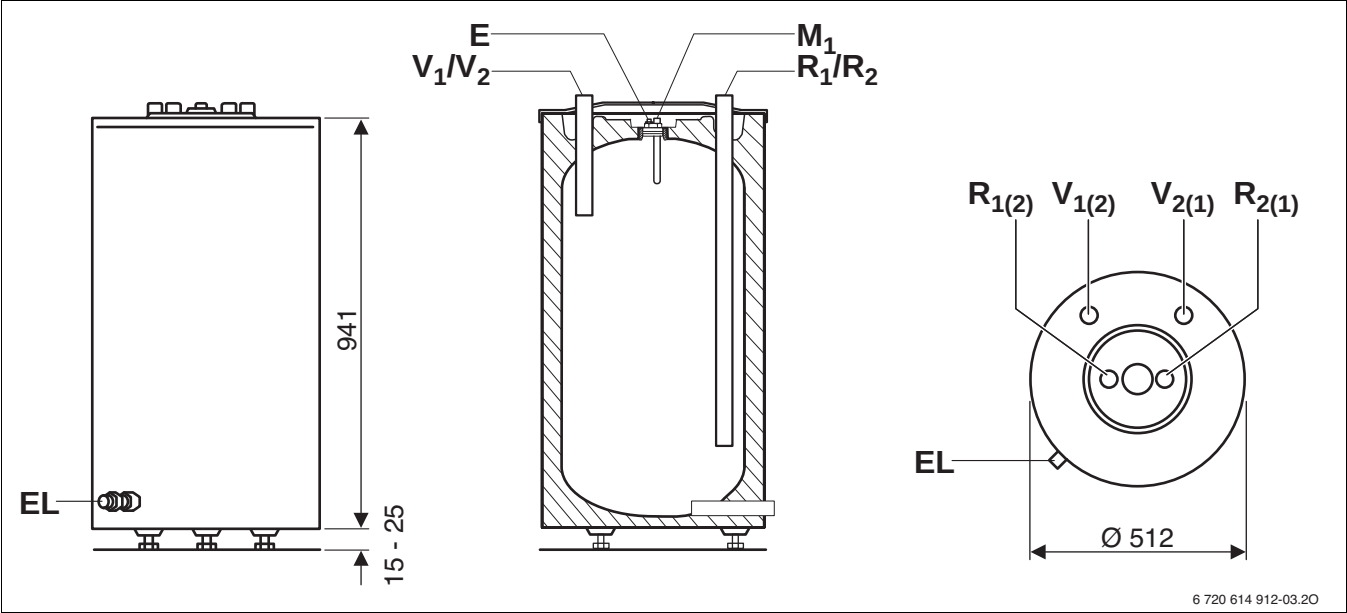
Bau- und Anschlussmaße (Maße in mm)
